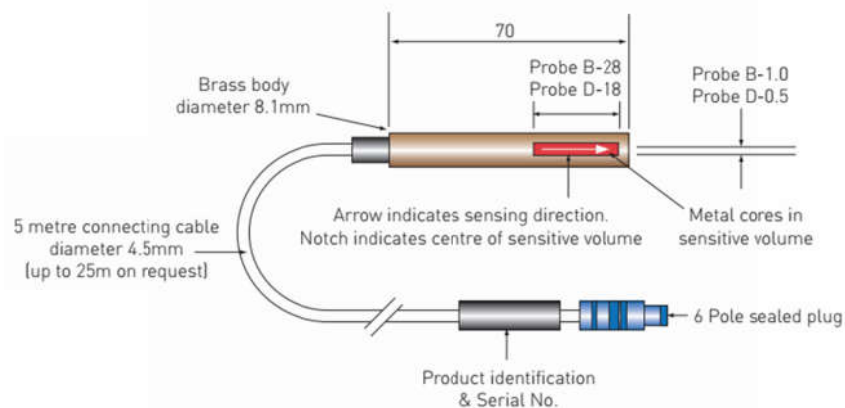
Punta de prueba axial del magnetómetro, las dimensiones están en milímetros.
